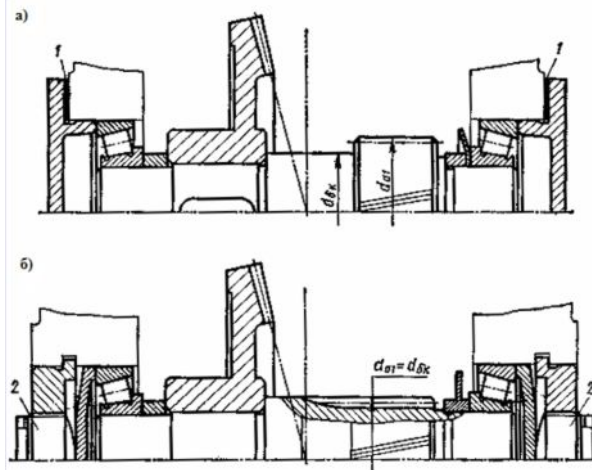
Примеры конструкций промежуточных валов коническо-цилиндрического редуктора
